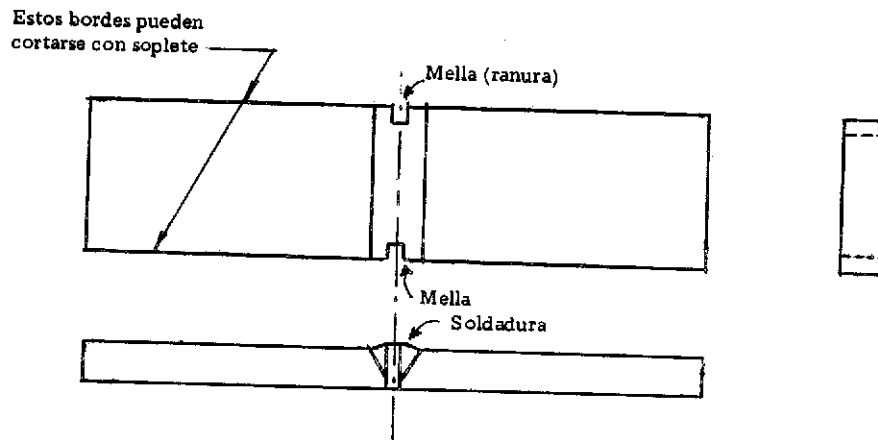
Especimen para ensayo de mella (planchas).
